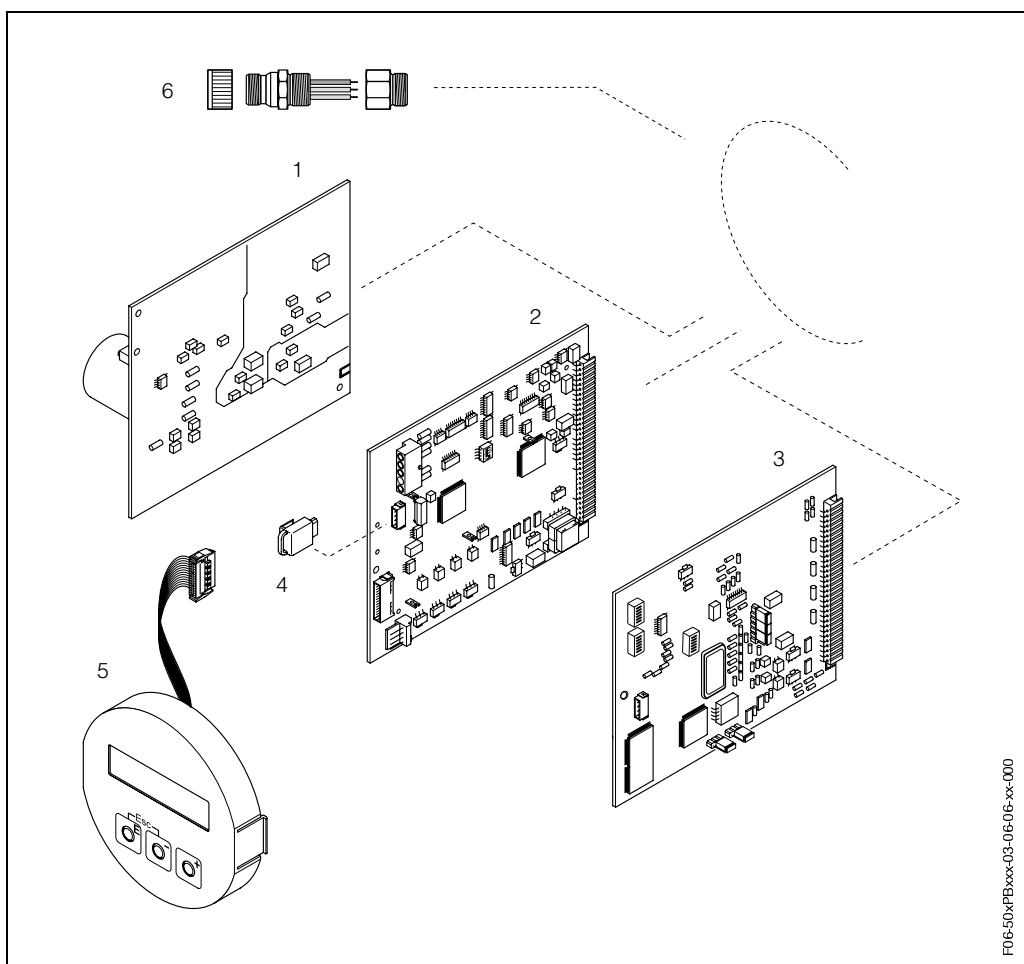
Piezas de recambio del transmisor Promag 50 (cabezal de montaje pared y de montaje en campo)
